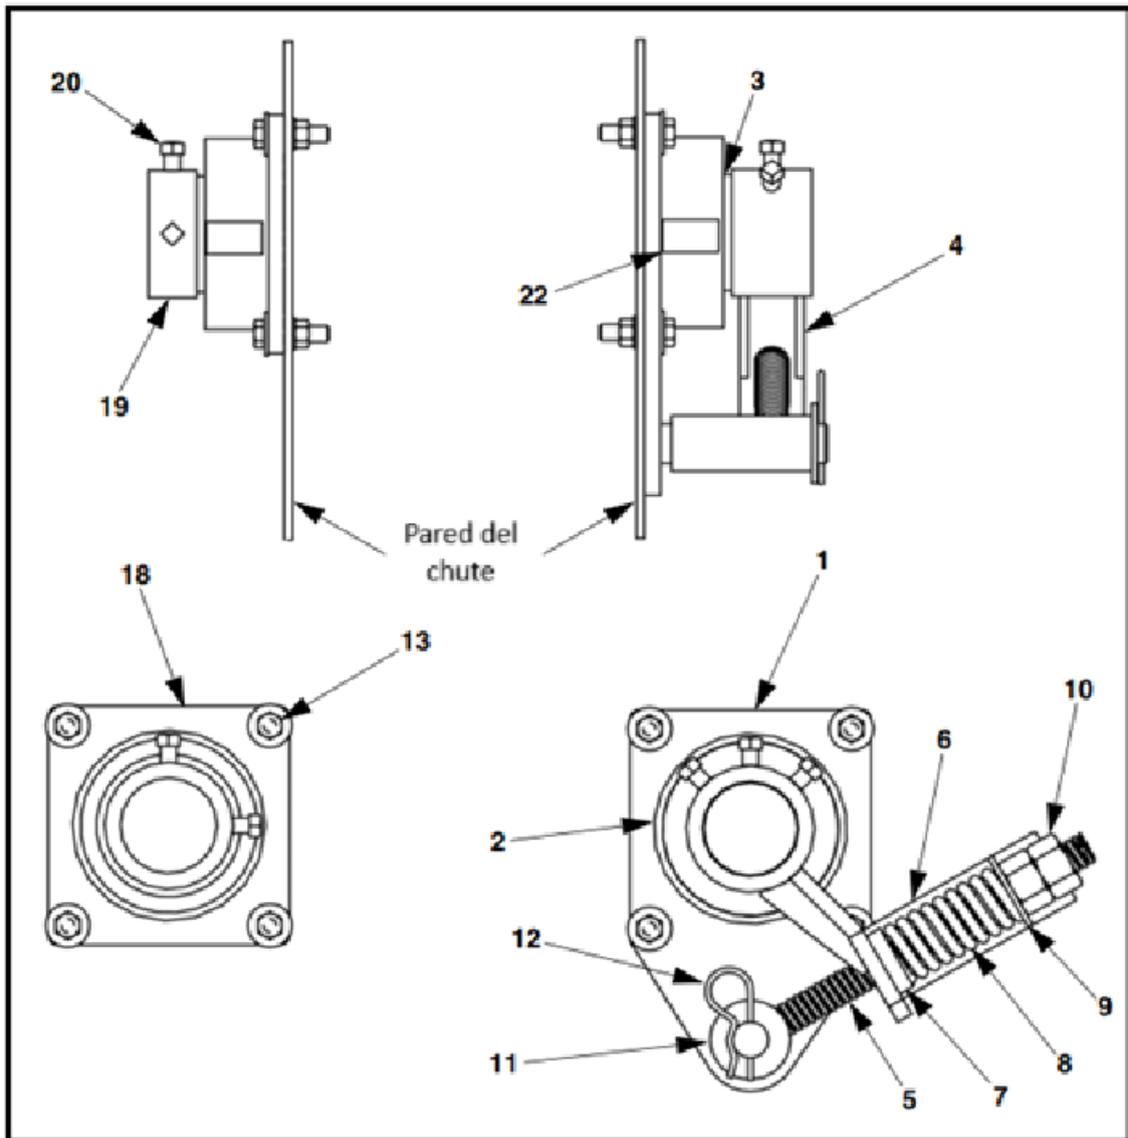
Ensamble del tensionador mecánico Martin ® HD Max: P/N 38947.
